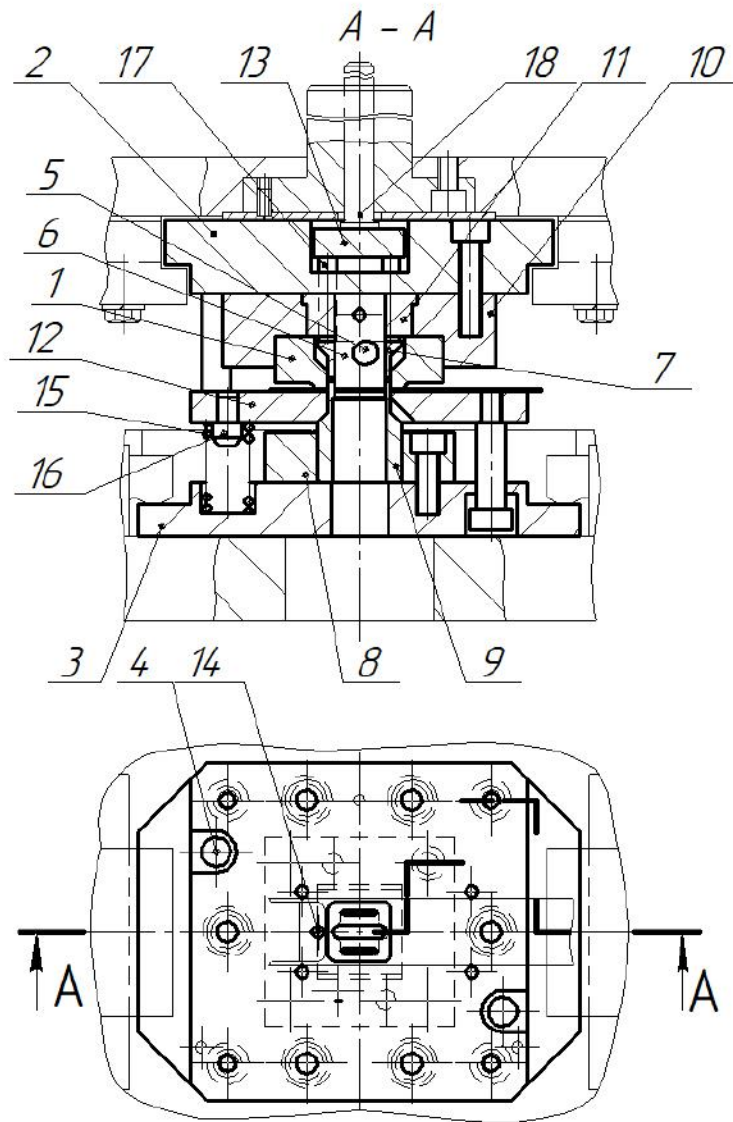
Схема пакету для блока швидкозмінного кріплення
